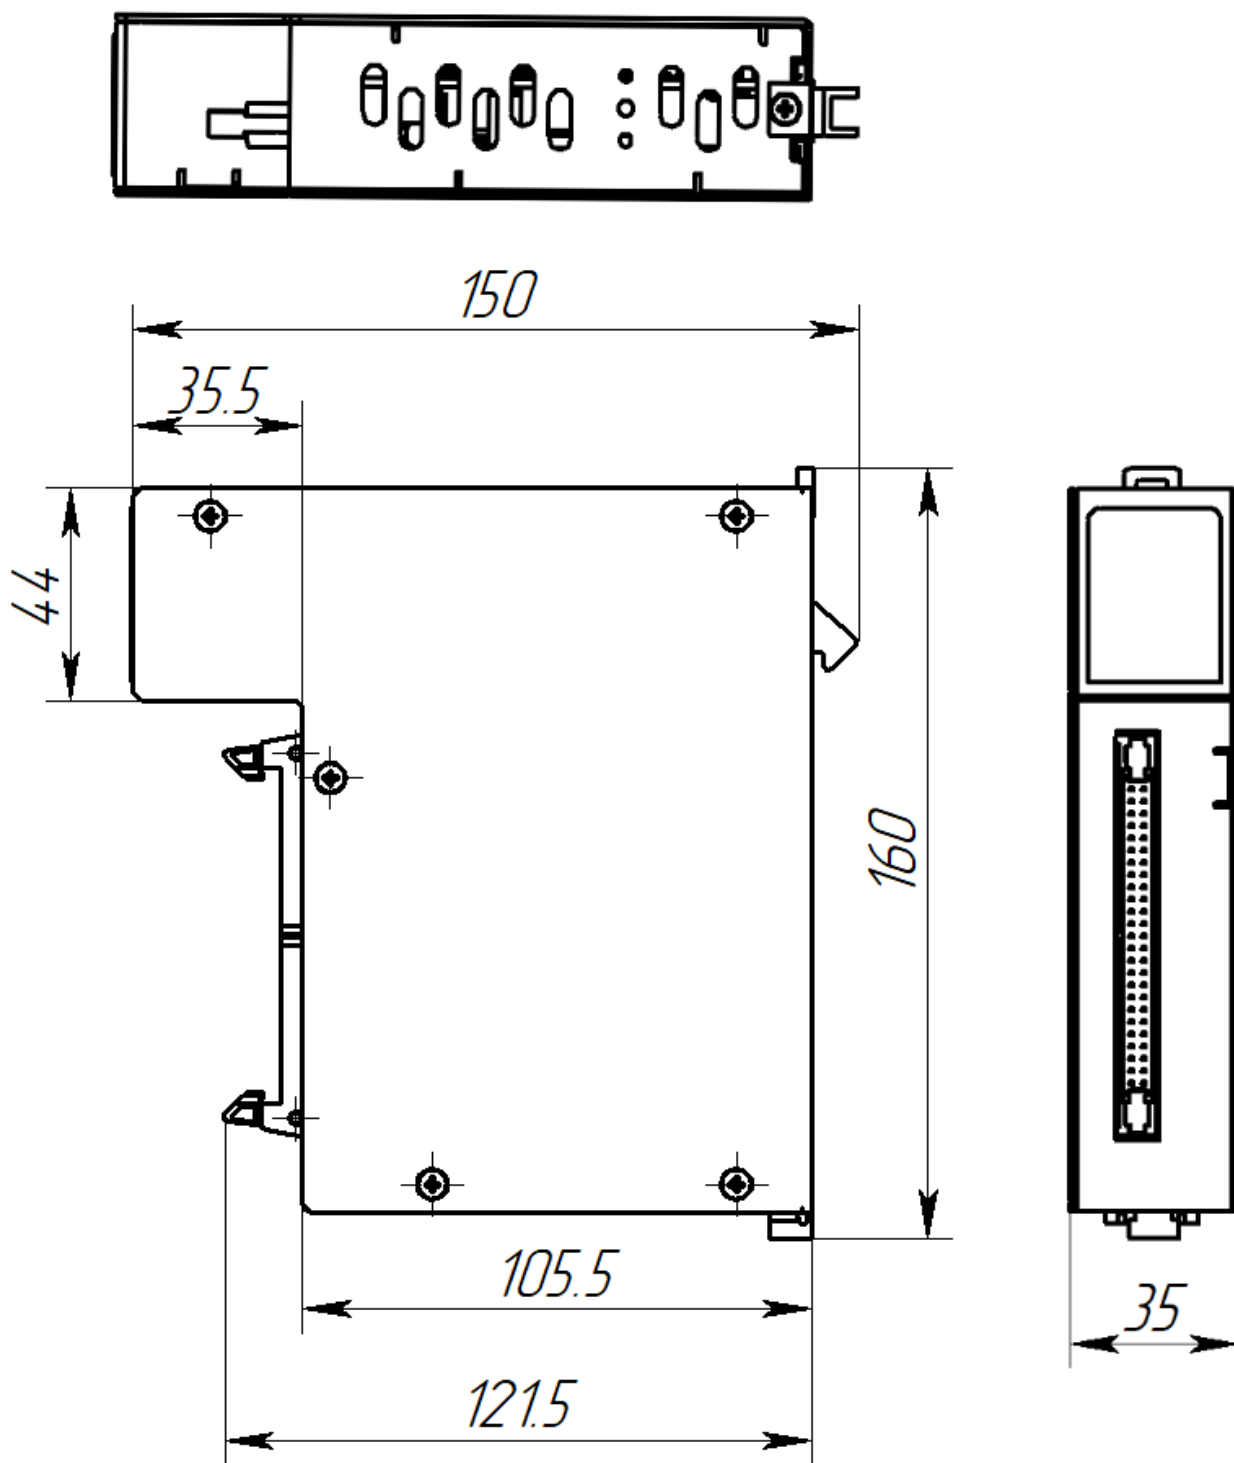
Габаритные и присоединительные размеры модуля ввода-вывода в металлическом корпусе
